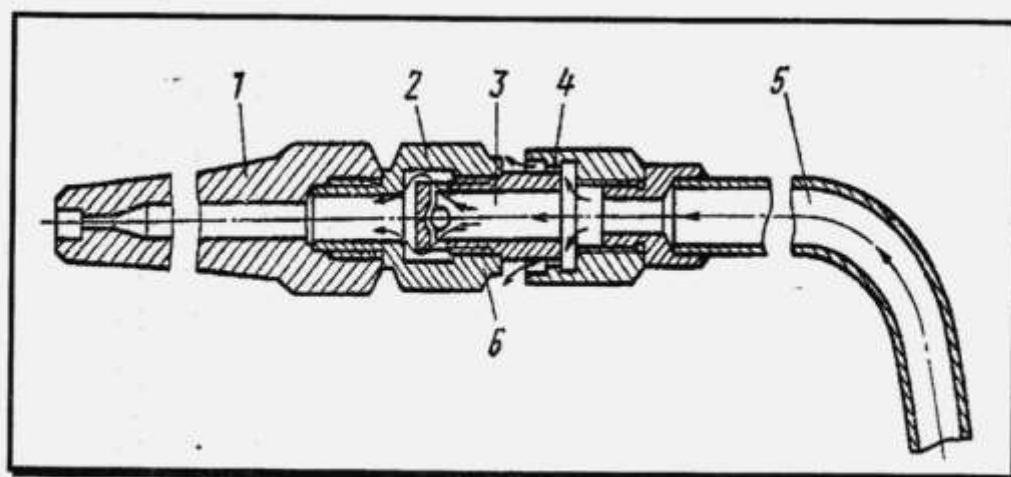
Наконечник с подогревателем для сварки на пропан бутане
